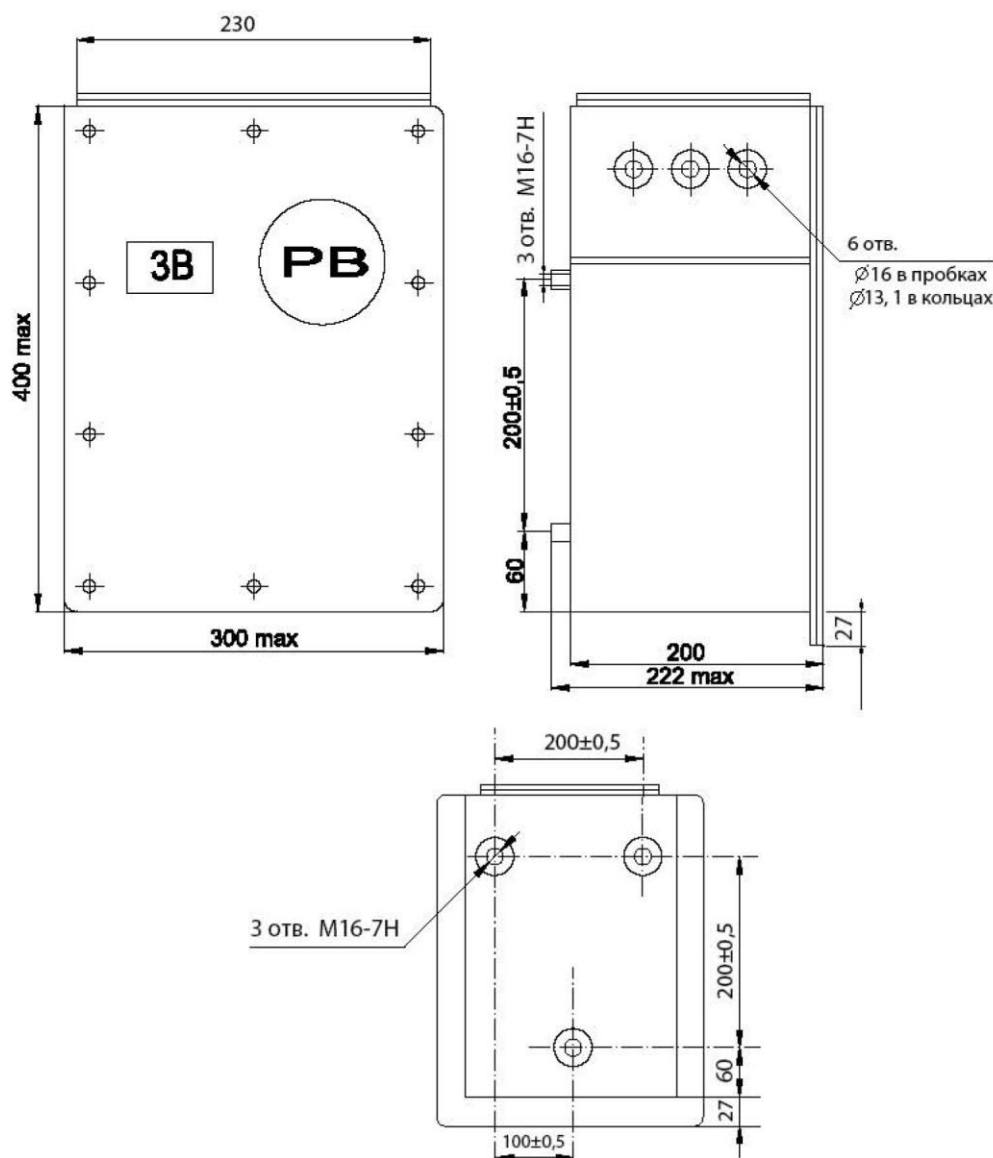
Габаритные и установочные размеры стабилизатора напряжения СНВ-2М
